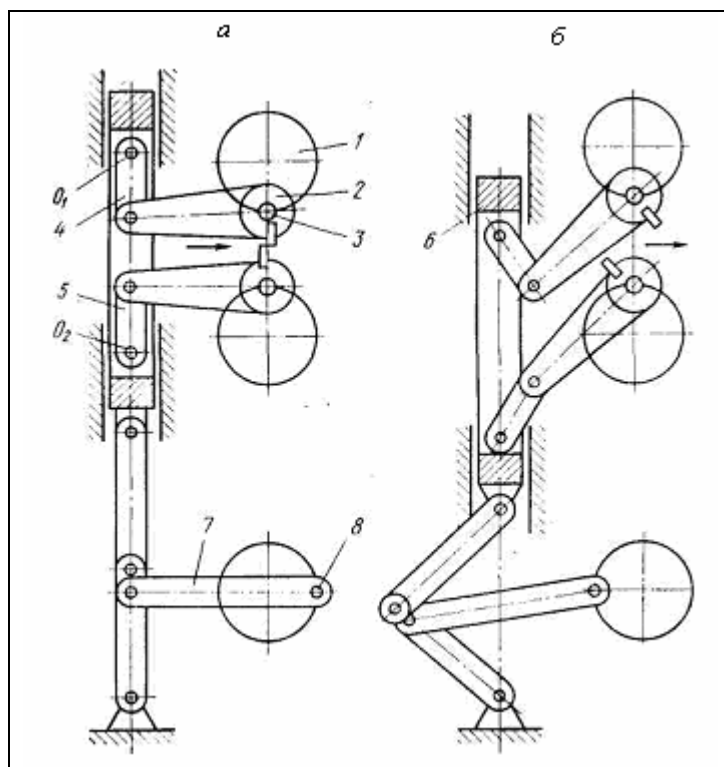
Схема режущего механизма летучих рычажно-кривошипных ножниц со скользящим кривошипом: а — момент реза; б — момент пропуска реза: 1 — барабаны; 2 — суппорты; 3 — кривошипы; 4, 5 — серьги; 6 — боковые штанги; 7 — шатунно-кривошипный механизм; 8 — нижний кривошип
